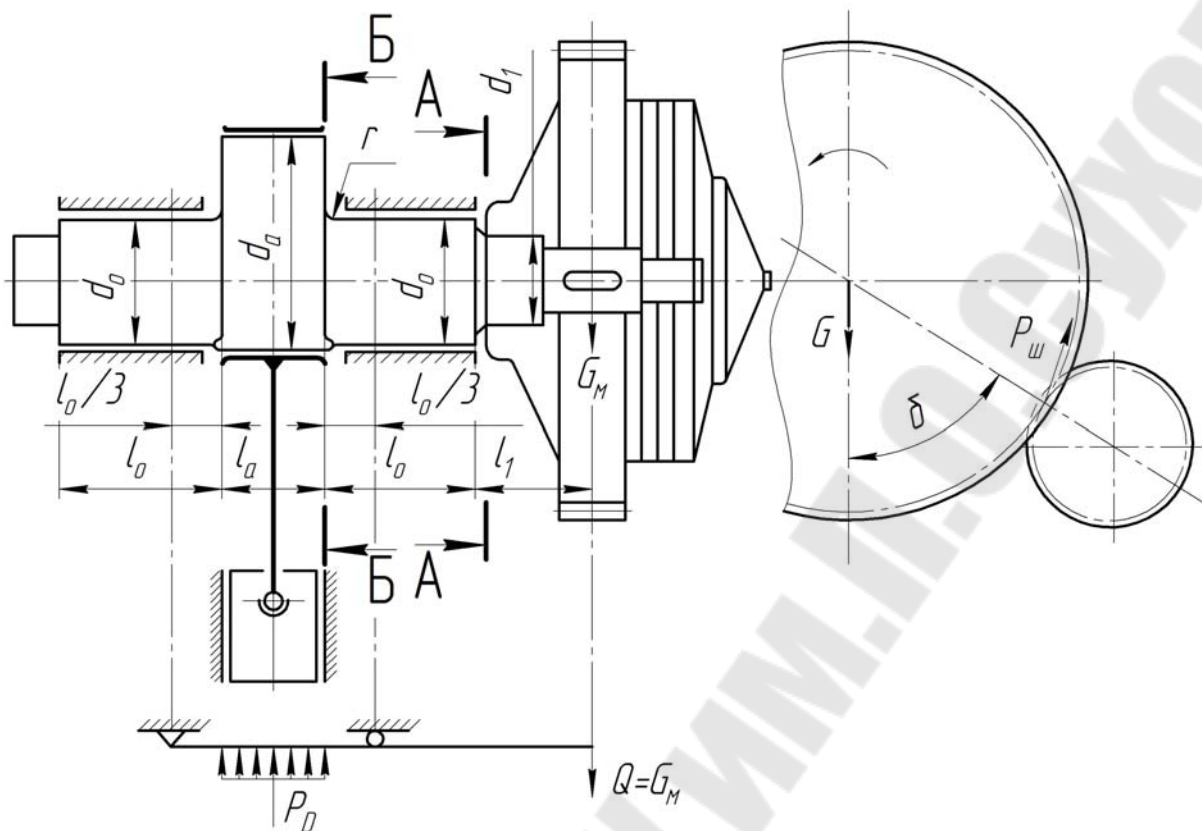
Коленчатый вал эксцентрикового типа с односторонним зубчатым приводом с муфтой
